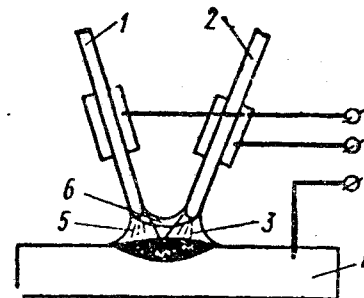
Сварка трехфазной дугой: 1, 2 — плавящиеся электроды; 3, 5, 6 — сварочные дуги; 4 — основной металл
